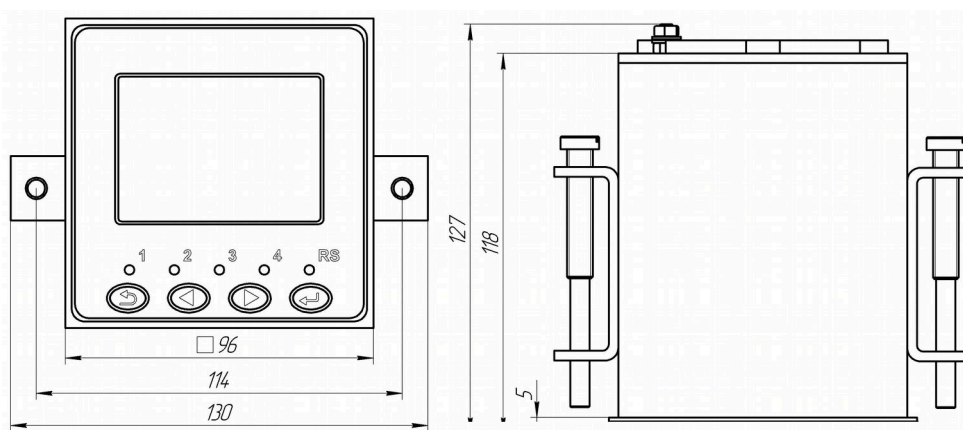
Габаритные размеры измерительного прибора АРК-5102 щитового монтажа.
